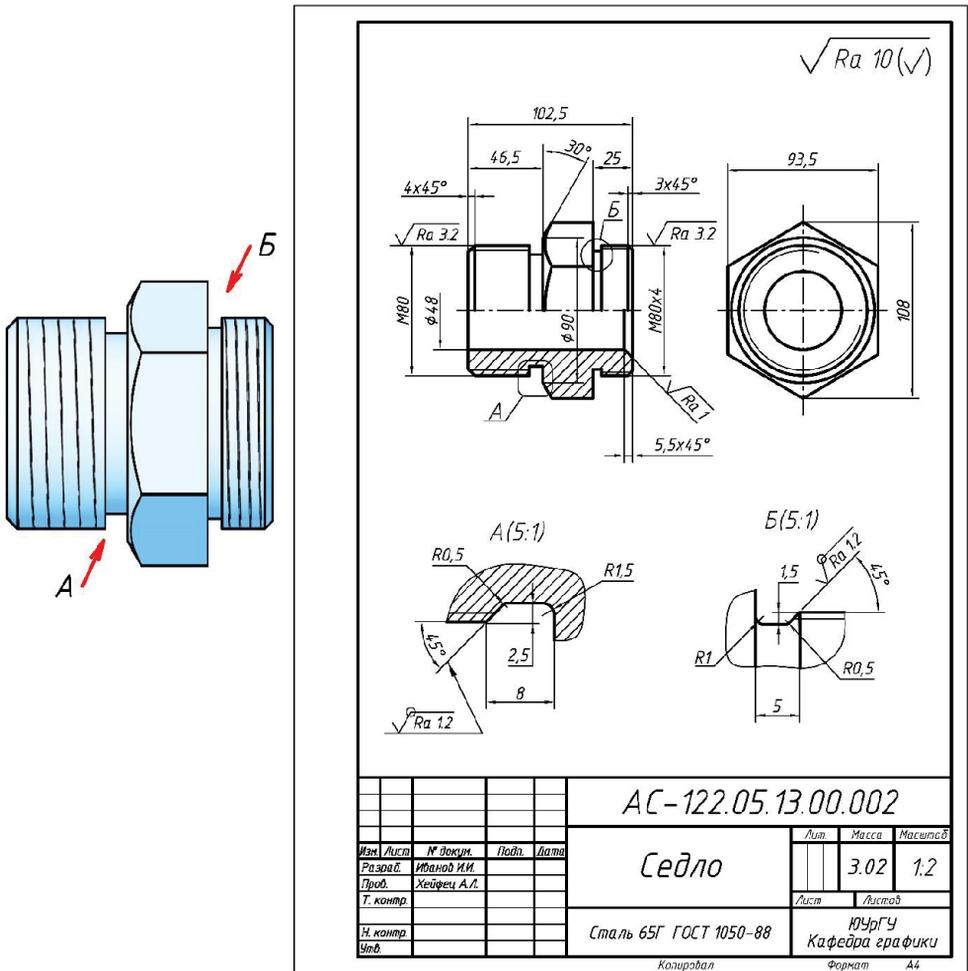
Модель и рабочий чертеж детали «седло»
